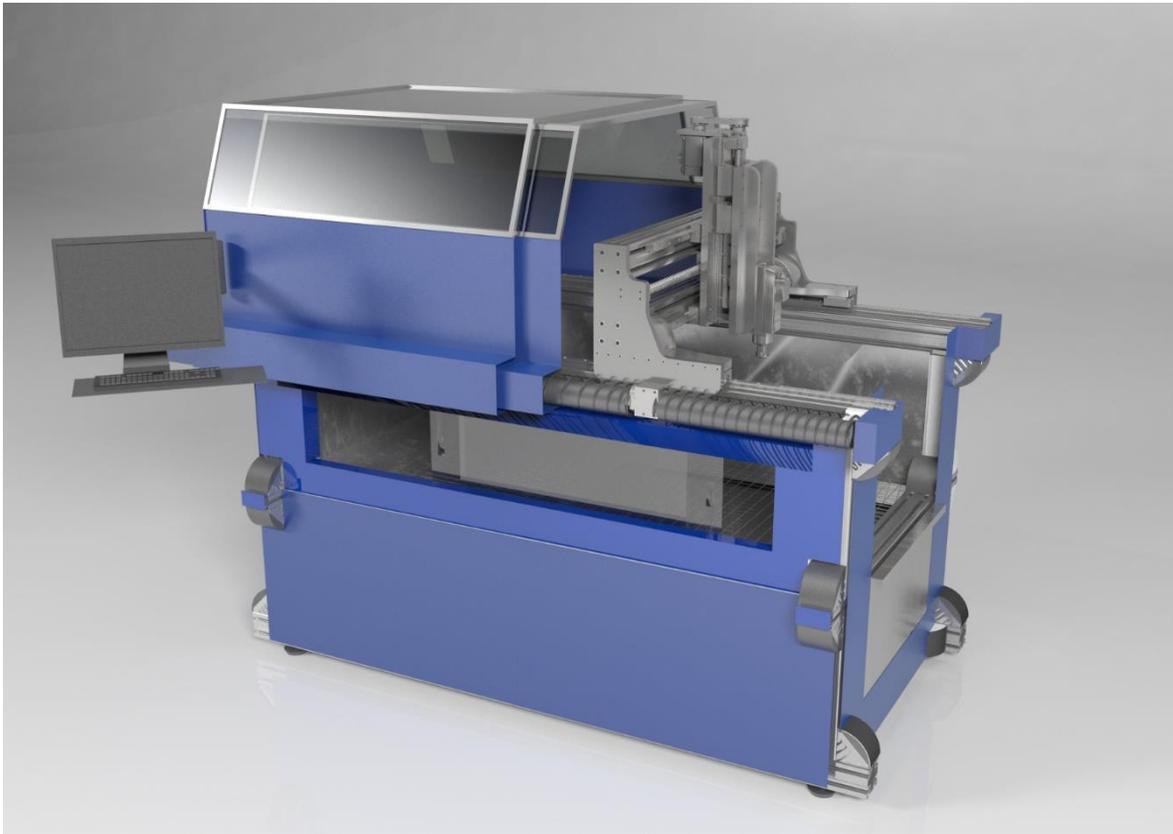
Máquina en condición posicionamiento de pieza y herramienta.
